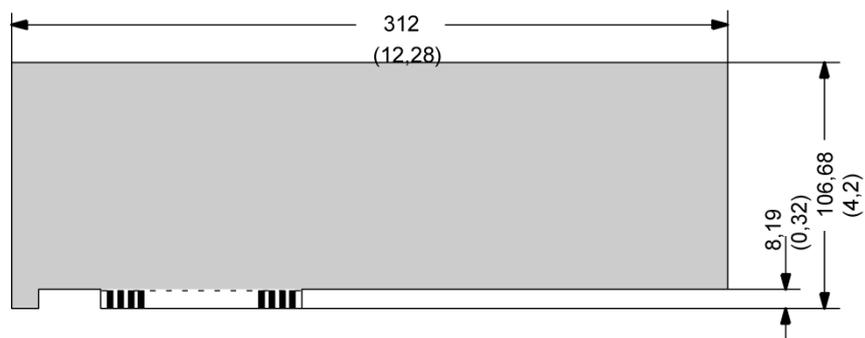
Maßbild für den Einbau ohne Einbauwinkel
